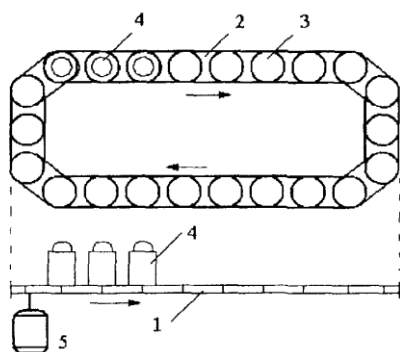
Схема пластинчатого транспортера: 1 - приводная цепь с пластинами; 2 - пластина типа; 3 - пластина типа; 4 - перемещаемый предмет; 5 - привод
